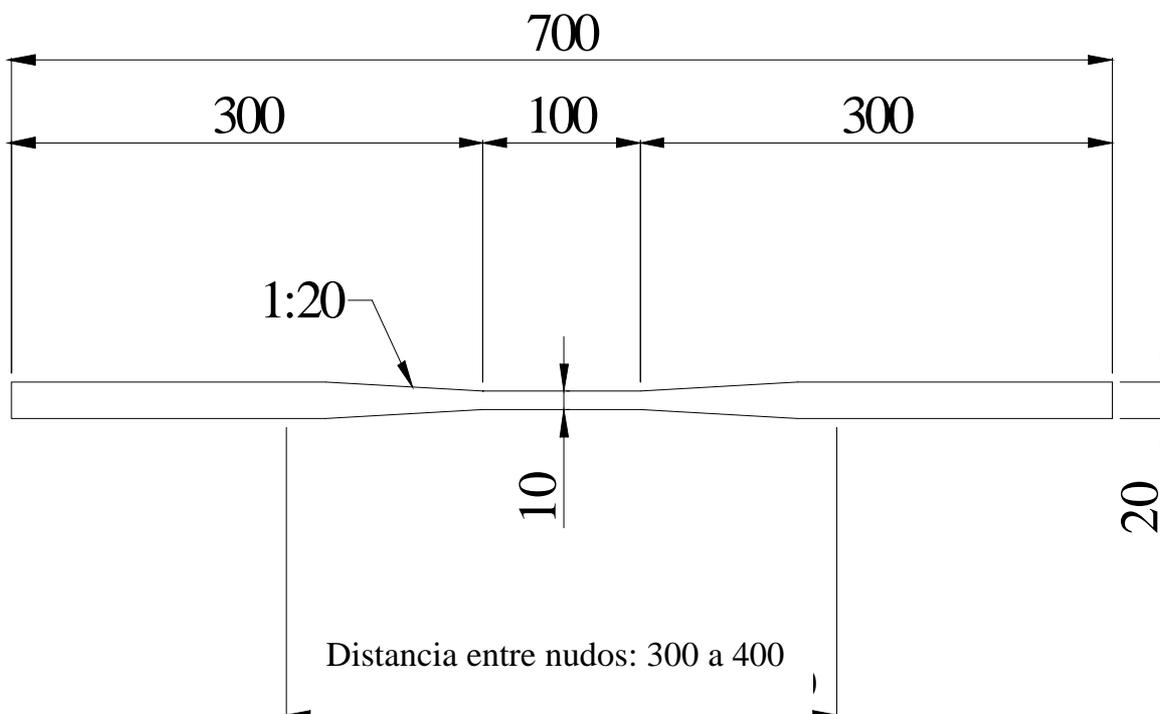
Pieza de ensayo para ensayos de tensión. Dimensiones en mm
